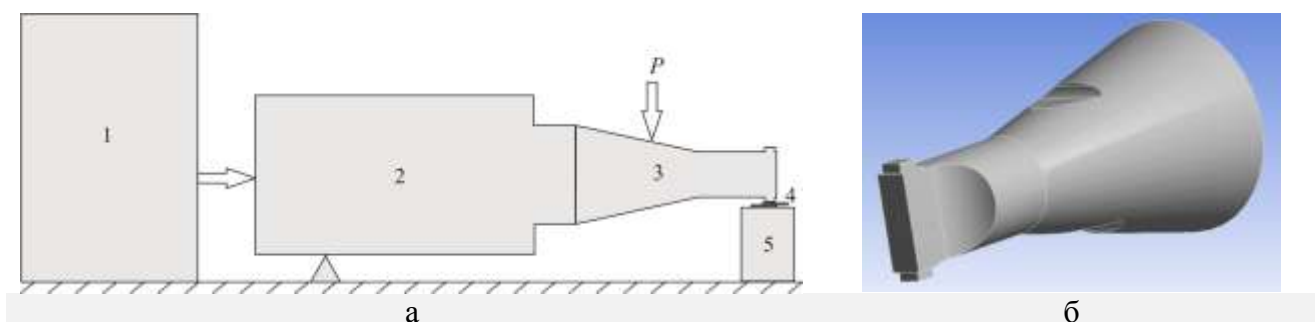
Схема установки для ультразвуковой сварки металлов: ультразвуковой генератор (1), ультразвуковой преобразователь (2), волновод (3), образцы (4), наковальня (5) (а) и вид сварочного волновода (б)
